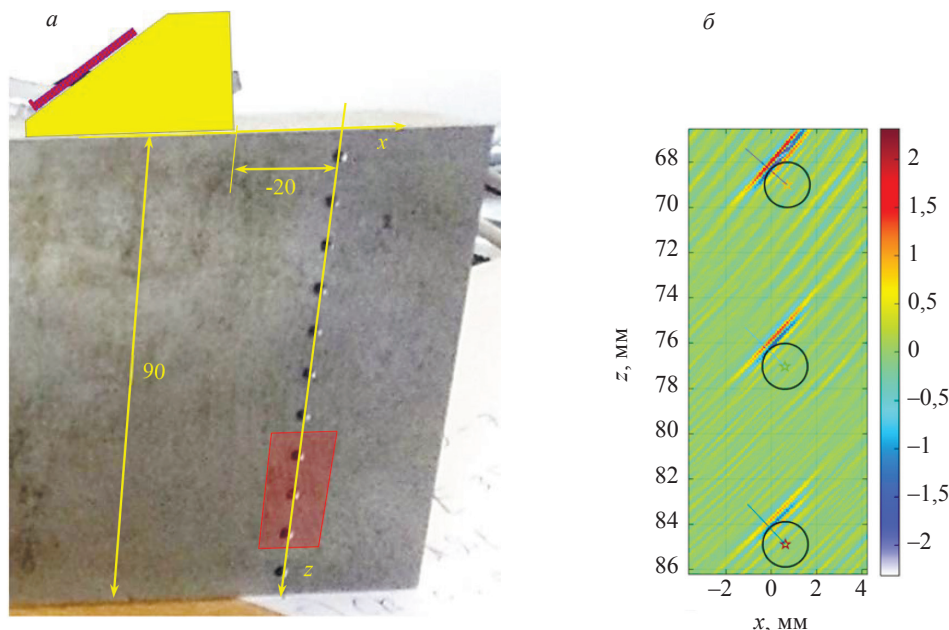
Вид образца НО-Ф2-П90-ПЛ-Б2 для проверки (а); фрагмент изображения в формате реального числа с контурами трех БЦО и контрольными линиями для получения среза блика границы (б).
